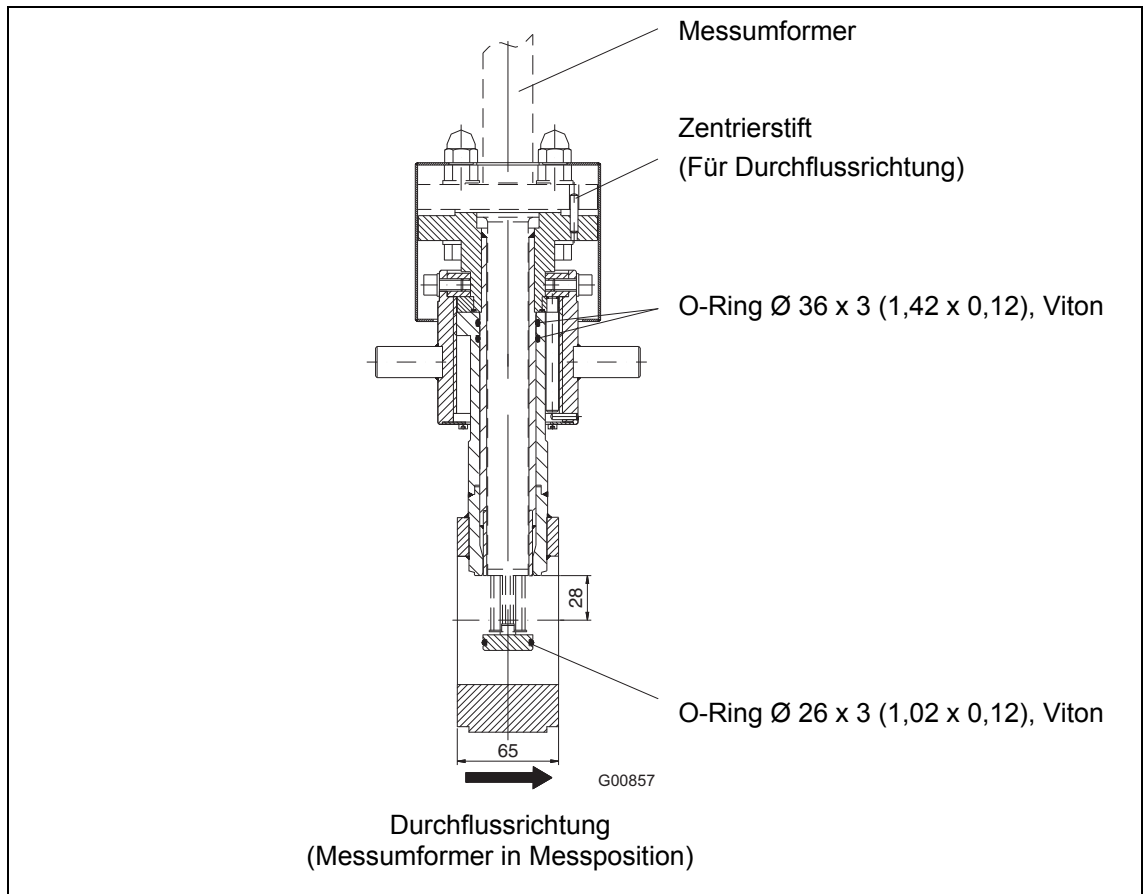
Maße in mm (inch). Wechselvorrichtung in Zwischenflanschausführung.
